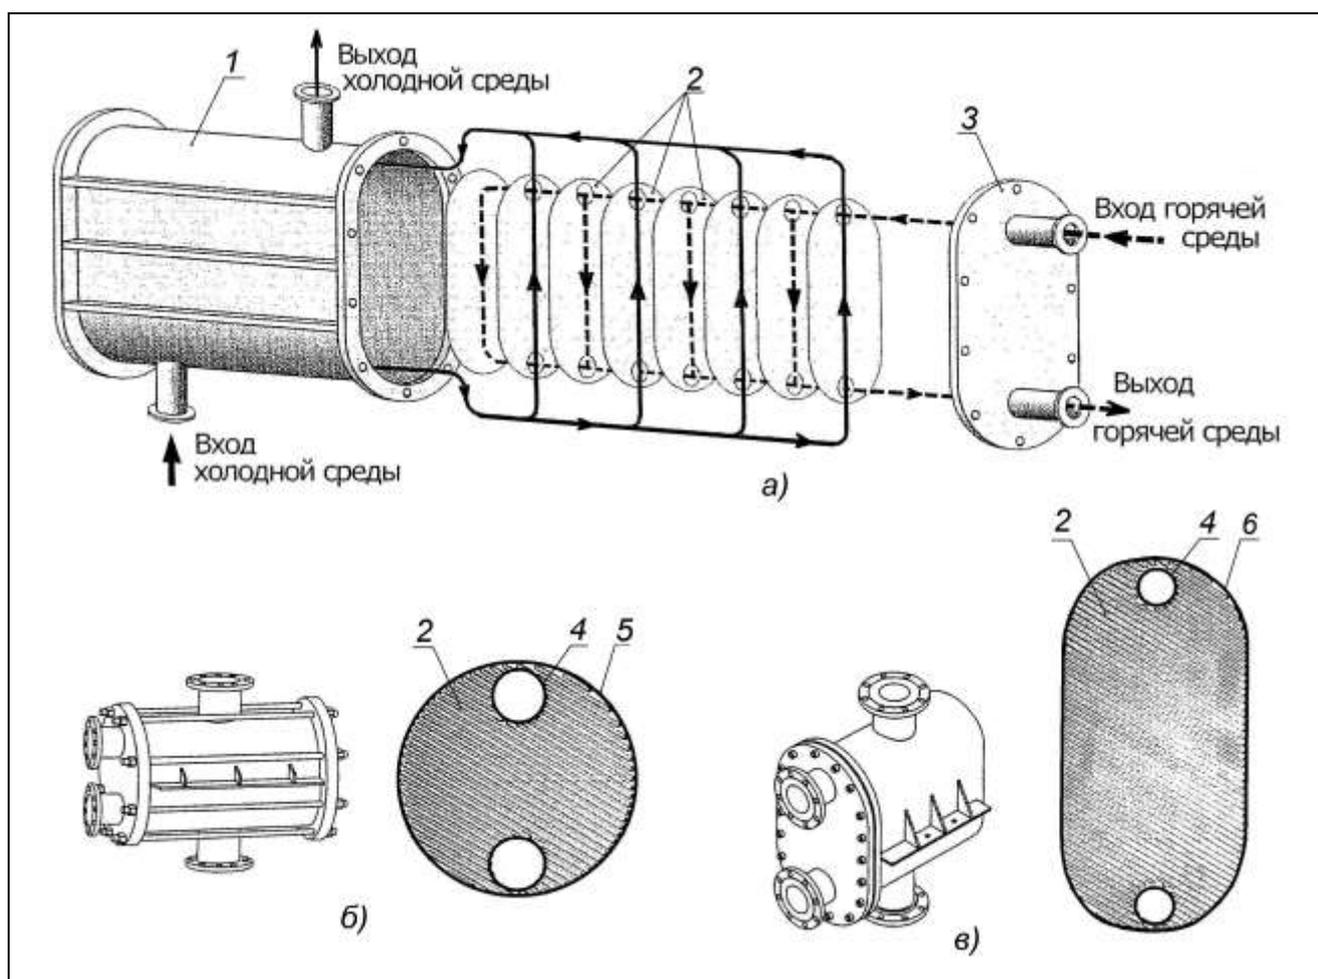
Устройство кожухопластинчатого теплообменника: а) – схема движения рабочих сред; б) – теплообменники с круглыми (дисковыми) пластинами (тип А); в) – с вытянутыми (овальными) пластинами (тип С)
